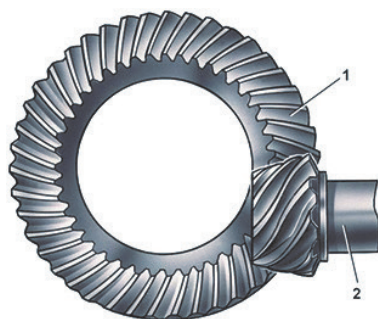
Конічні гіпоїдні шестерні: 1 — ведена шестерня, 2 — тягова шестерня
